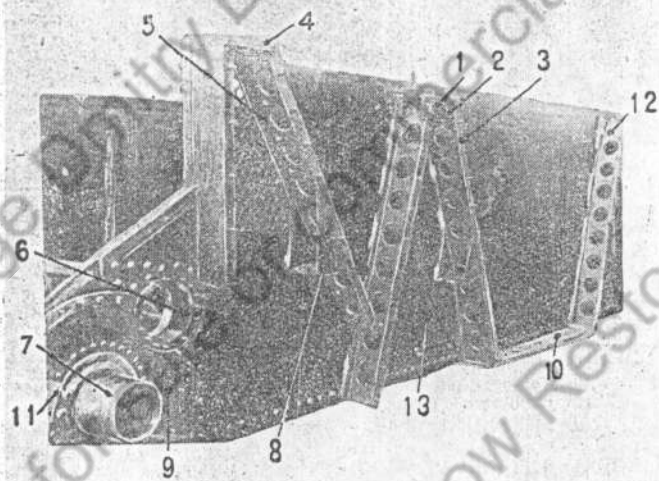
Вид на заднюю часть корпуса со снятой бортовой броней.
